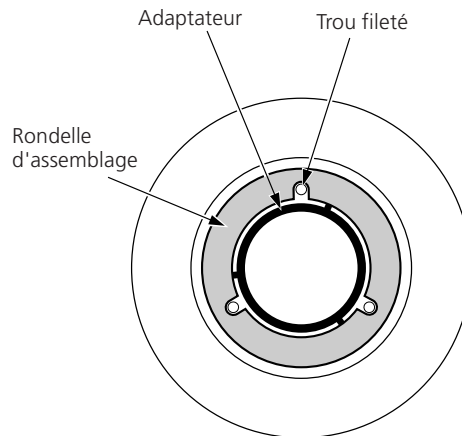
Installation des fentes de la rondelle d'assemblage sur les trous filetés
